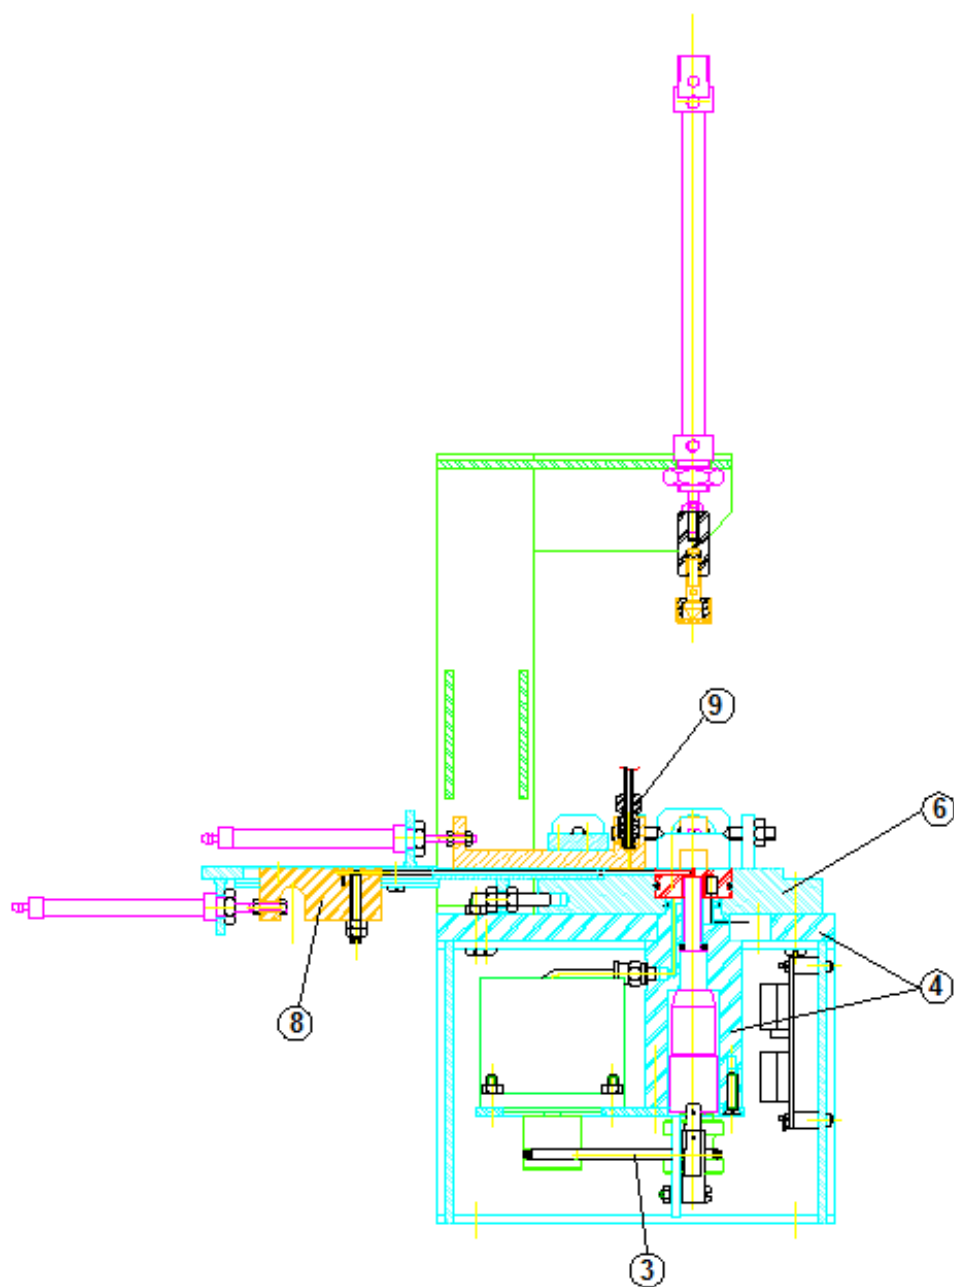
Corte lateral do dispositivo de soldagem constituído por: correia (3), base (4), base de ajuste (6), suporte de agulha de fixação (8) e conexão da mangueira do inversor de tubos de titânio (9)
